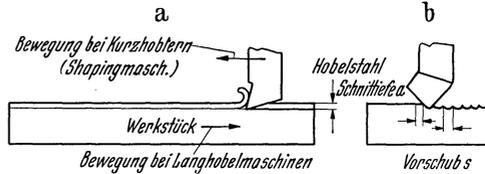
Geradlinige Bewegungsrichtung an Hobelmaschinen.
